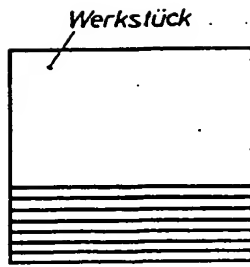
Tiefenstaffelung der Schneidzähne beim Plan-Räumwerkzeug
